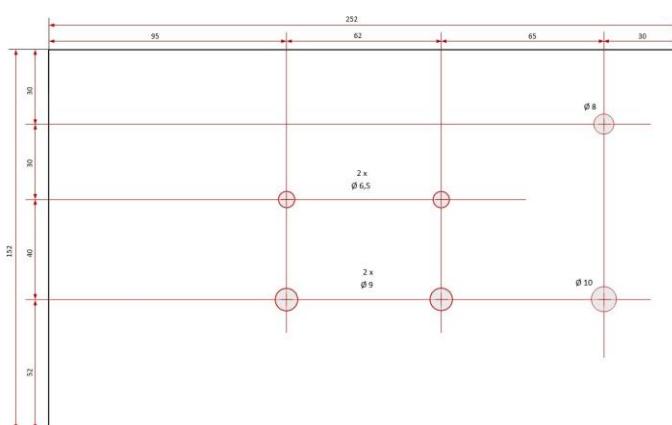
dessins de l'usinage de la face avant (à gauche) et de la face arrière (ci-dessus)
